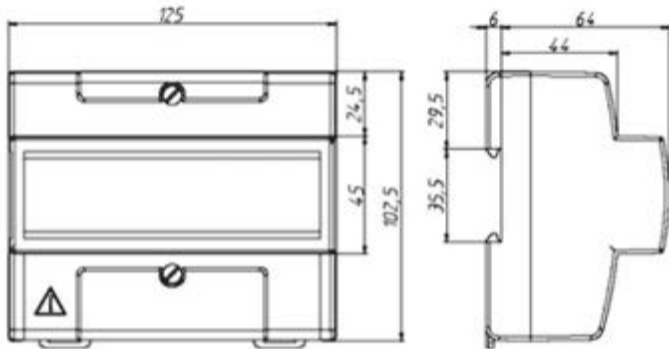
Счетчики в корпусе D33 для установки на DIN-рейку
